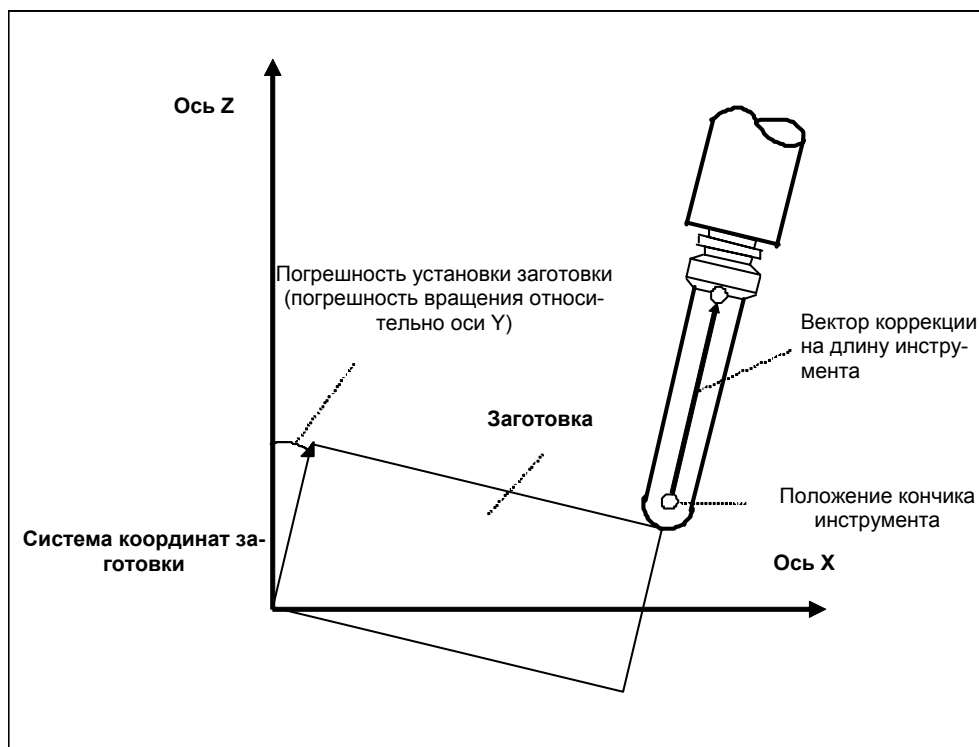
(f) Резка вершиной инструмента, когда имеется погрешность установки заготовки (если RCM=1)
